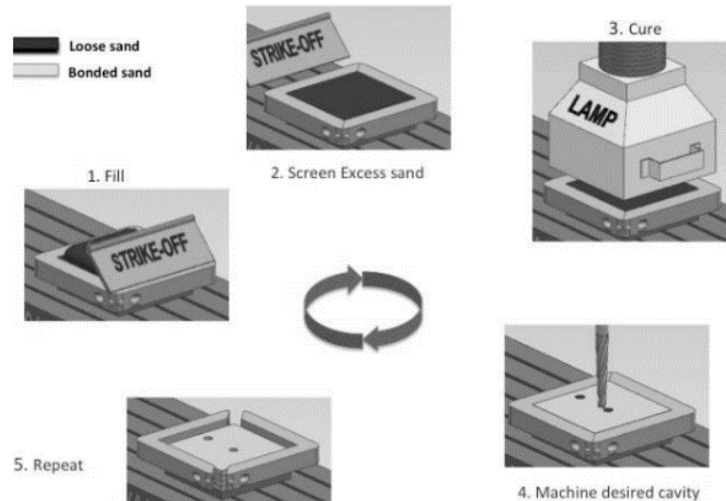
Principe du procédé hybride de fabrication de moule en sable [IKO16]
